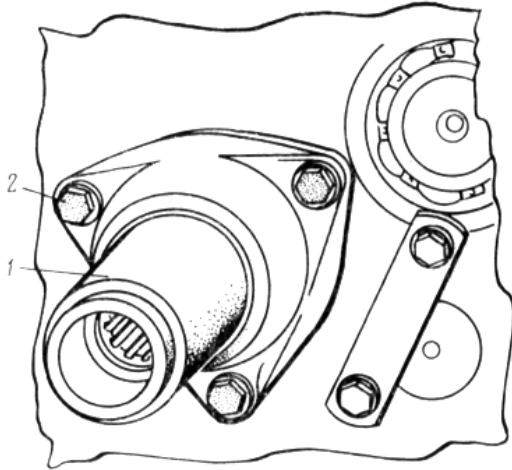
Знімання гнізда внутрішнього вала: 1- гніздо внутрішнього вала; 2- болт
